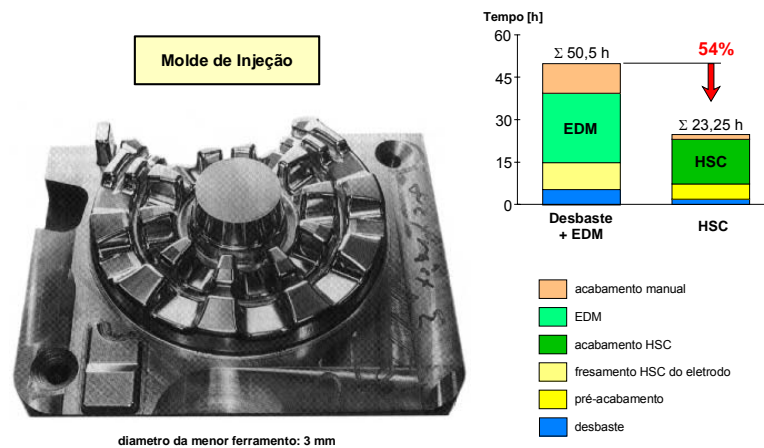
Manufatura de um molde de injeção [48, 49].
